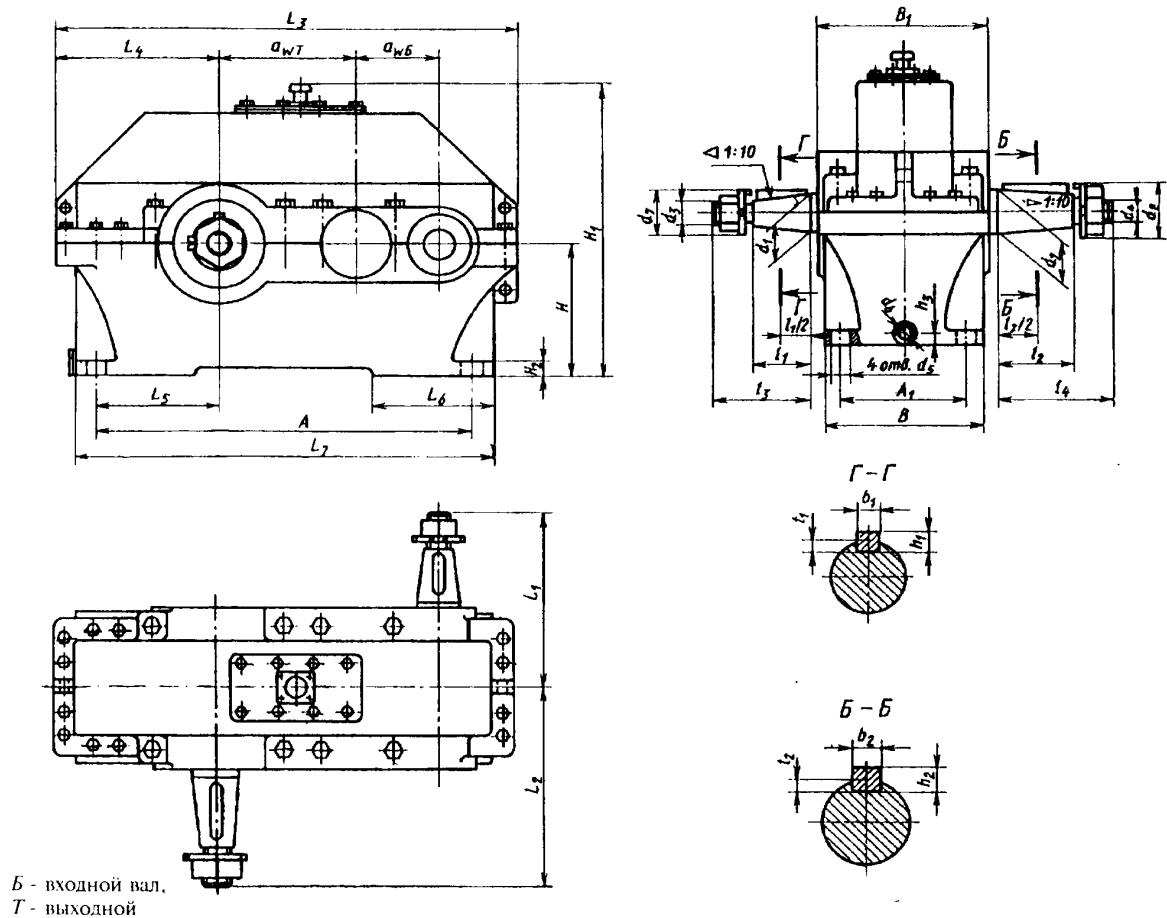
Цилиндрический двухступенчатый редуктор Ц2У-160
